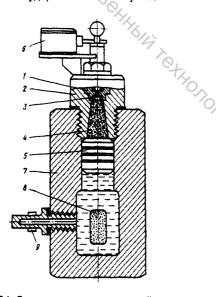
Схема гидродинамической установки 1 – ударный механизм; 2 – резьбовой затвор; 3 – капсюль-воспламенитель; 4 – пороховой заряд; 5 – поршень; 6 – электромагнит; 7 – корпус; 8 – прессовка; 9 – датчик давления
